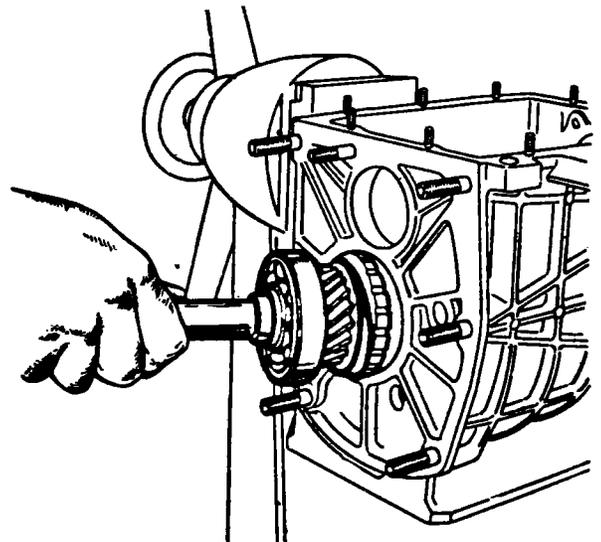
Извлечение первичного вала из картера коробки передач
